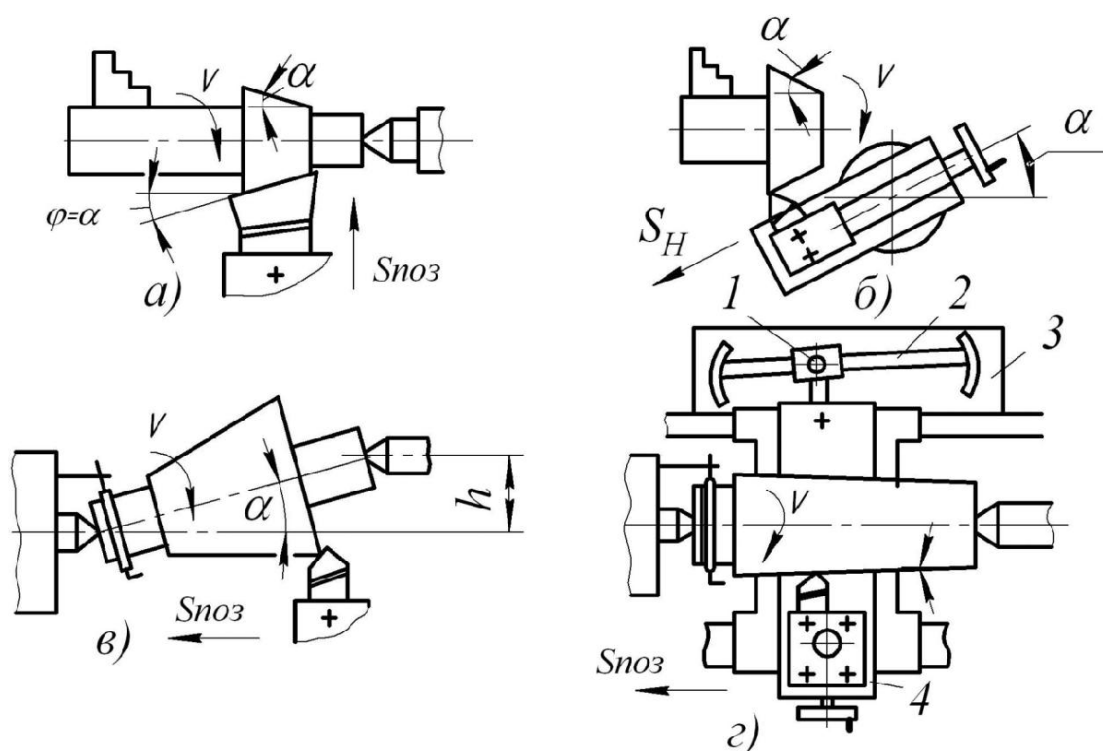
Схеми обточування зовнішніх конічних поверхонь на токарних верстатах
